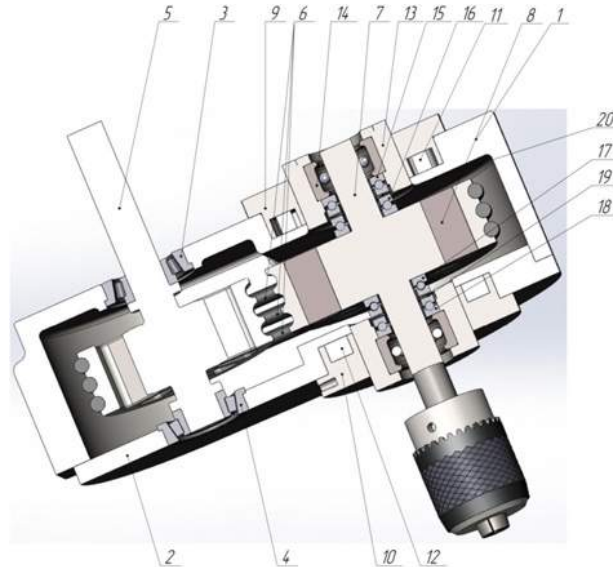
Устройство для вибрационного сверления: 1 – корпус 2 – крышка корпуса; 3,4 – подшипники; 5 – входной вал; 6 – гибкая связь; 7 – выходной вал; 8 – магниты; 9, 10 – магнитные корпуса; 11, 12 – магниты; 13 – гайка; 14 – подшипник; 15, 16, 17, 18 – упорные подшипники; 19, 20 – пружины
